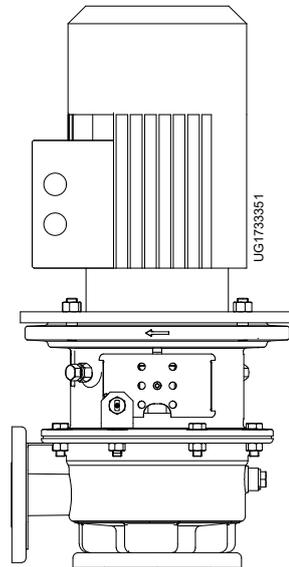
Modelo de lavadora de botellas, desde el tamaño de motor 80 = 0,55 kW hasta 180 = 22 kW
